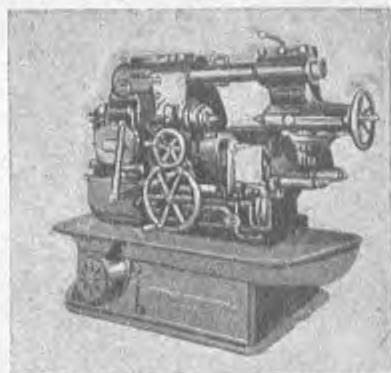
Многорезцовый токарный станок МТ-30. Максимальный диаметр обрабатываемого предмета 350 мм. Число скоростей шпинделя 12
